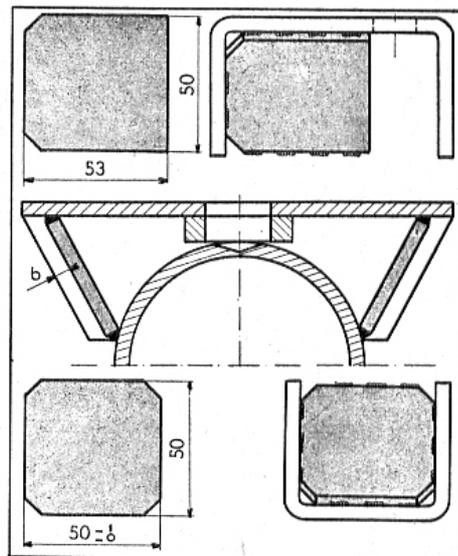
En haut à gauche : Plaque de renfort 6.053.900. — A droite et au centre : Comment souder les plaquettes 6.053.900. — En bas à gauche : Plaquette pour patin étroit. — En bas à droite et au centre : Soudure des plaquettes sur patin étroit
